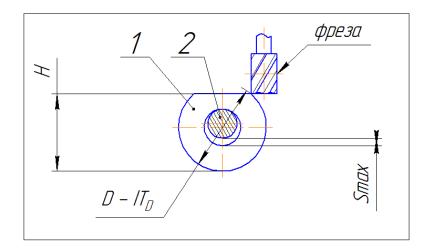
Установка на цилиндрический палец (охватываемой поверхностью), конструкторская база – нижняя образующая цилиндра D. оси заготовки 1 и оправки 2 не совпадают
